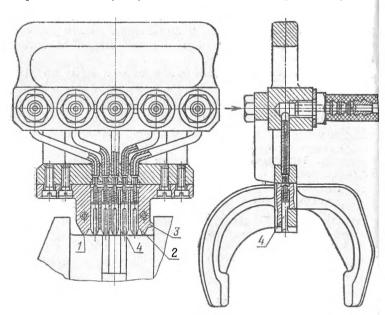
Приспособление для контроля прямолинейности образующих шеек коленчатого вала:
